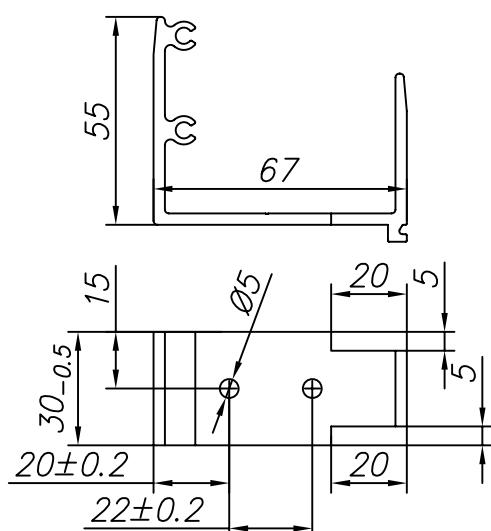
Изготовление соединителя FLGU 400.0911
